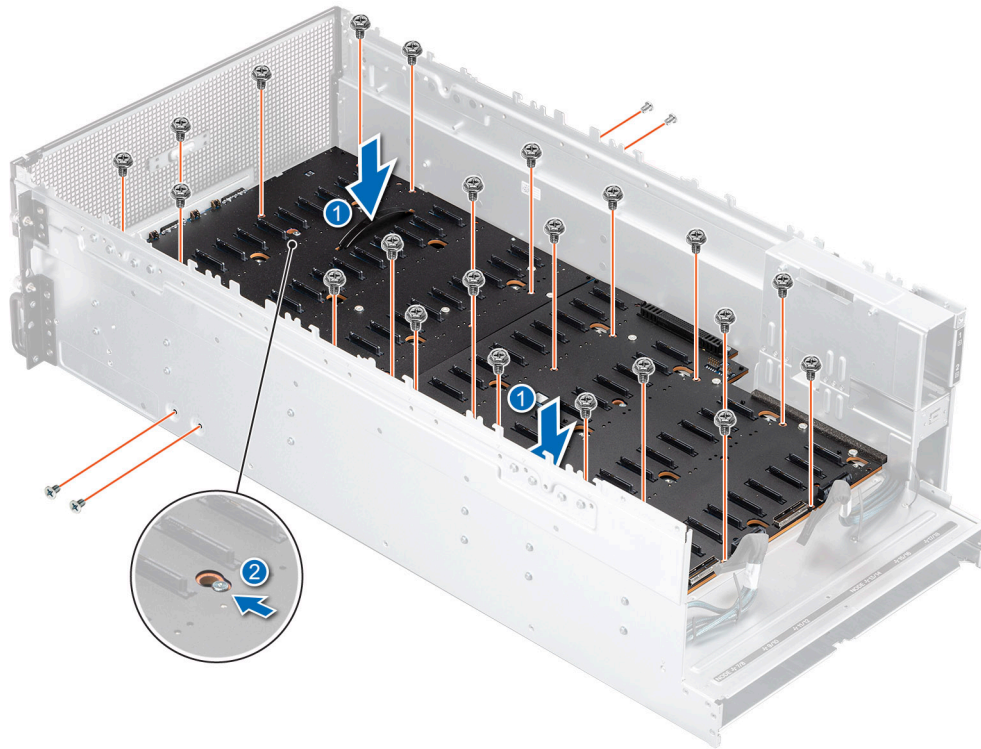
Installation de l'assemblage de fond de panier / fond de panier central
